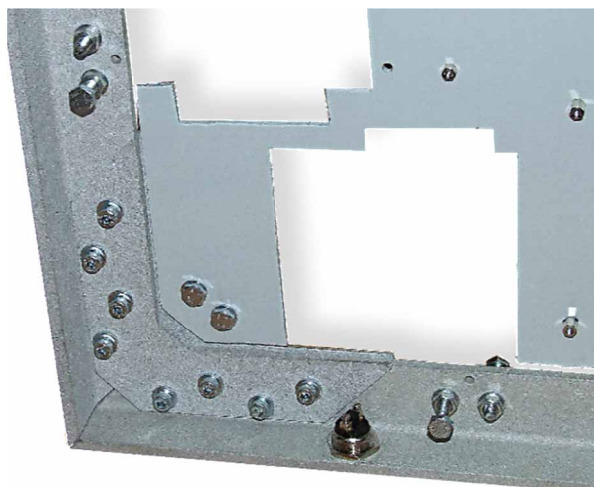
Detail konstrukce se středovou deskou a tlačítkem
